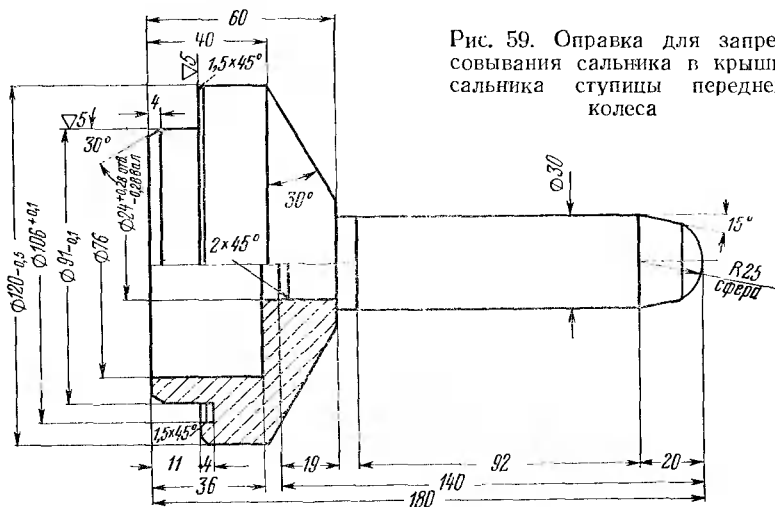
Оправка для запрессовывания сальника в крышку сальника ступицы переднего колеса
